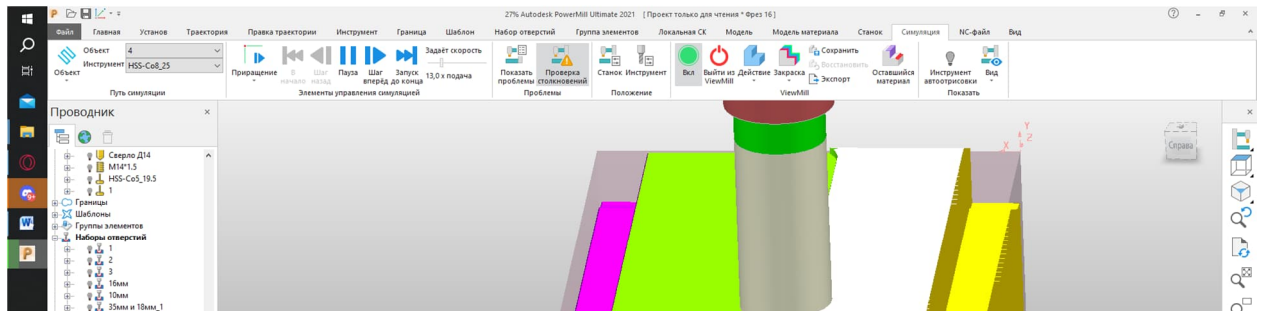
Фрезерування центрального отвору з пазом
